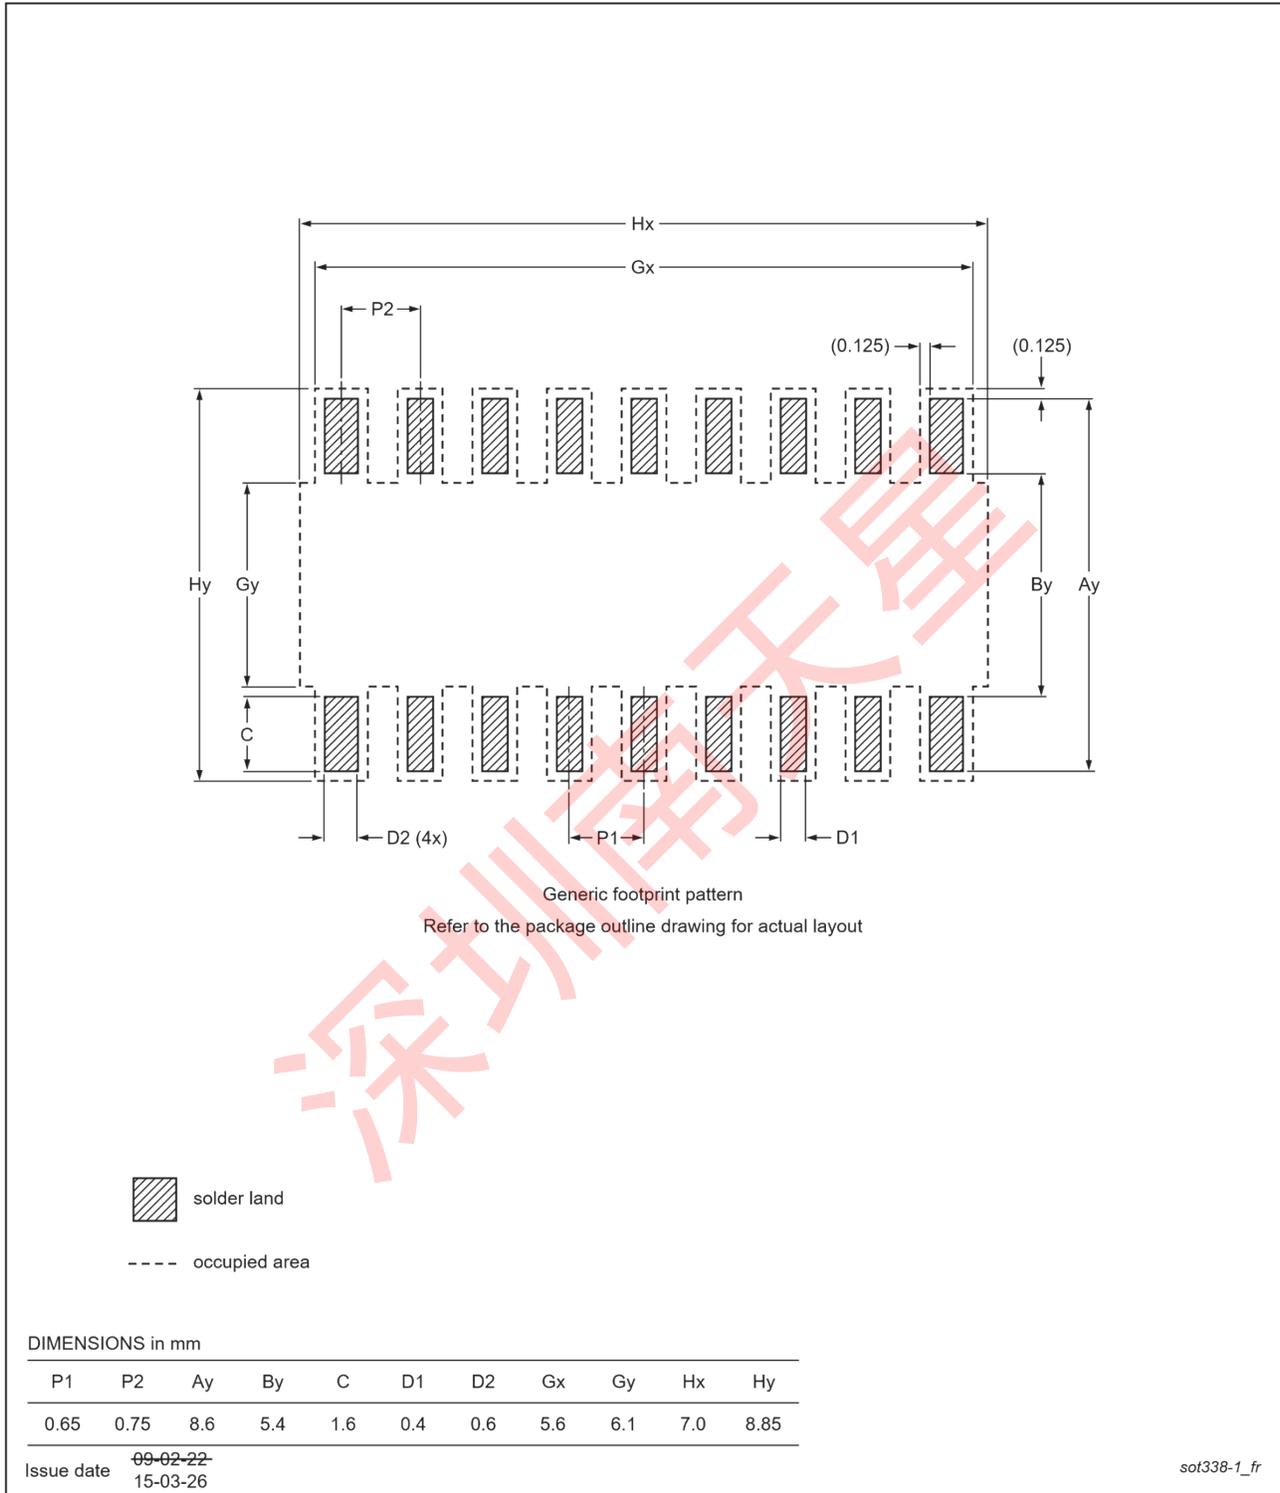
SOT338-1 (HVQFN16) 的 PCB 占地面积; 回流 soldering
